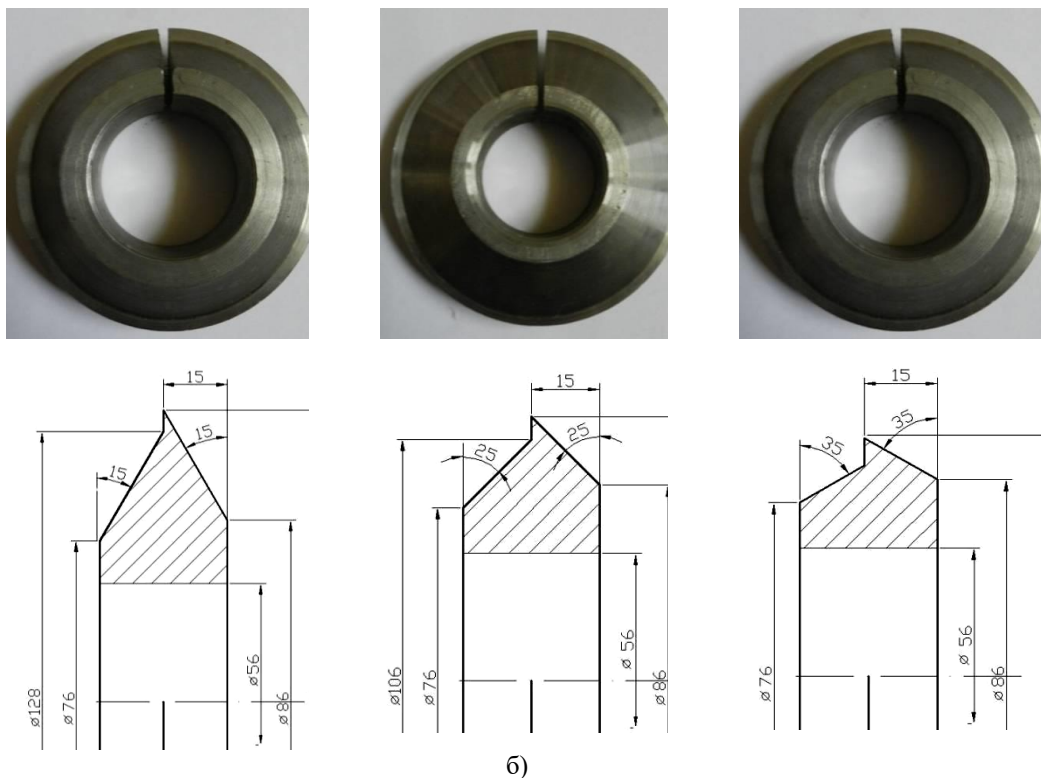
Формувальні втулки: а) загальний вигляд; б) конструктивні схеми
